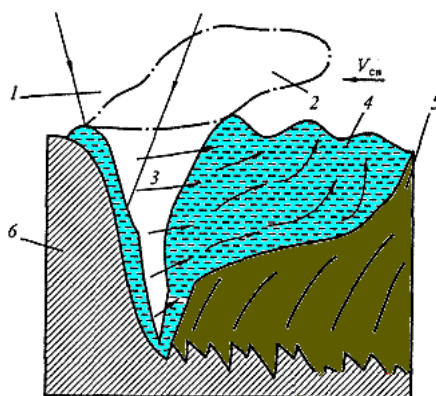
Схема сварочной ванны при лазерной сварке:
